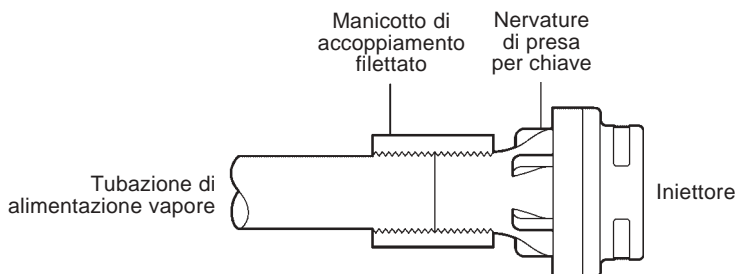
Iniettori IN25M e IN40M filettati - Tipica installazione con montaggio diretto sulla tubazione
